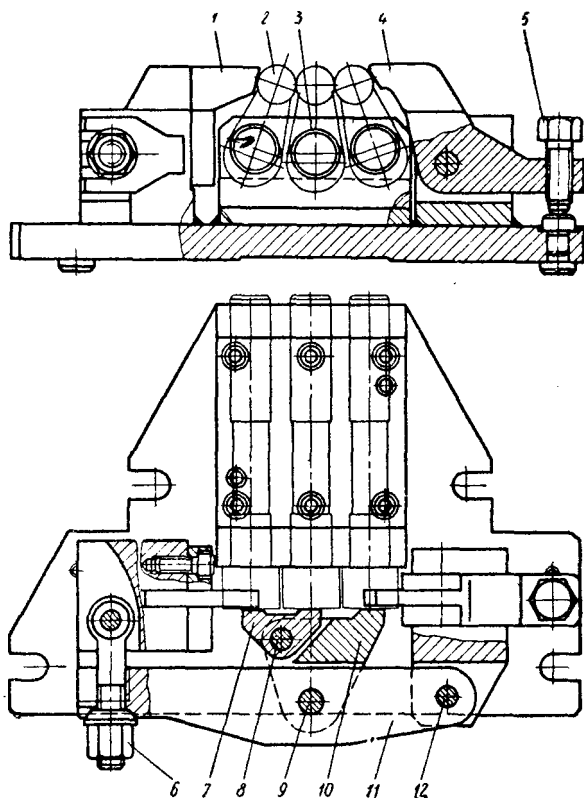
Трехместное приспособление для фрезерования головки деталей технологического ряда ВР-01
